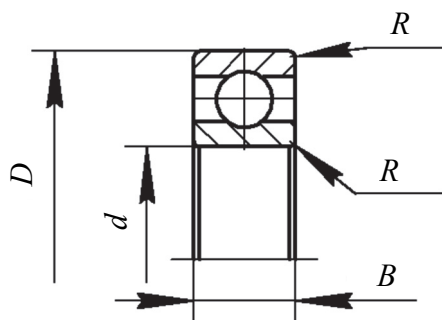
Габаритные размеры шариковых радиальных однорядных подшипников (по ГОСТ 8338–75)
